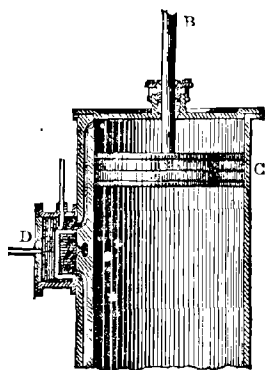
Coupe du cylindre et du piston d'une machine à vapeur.
